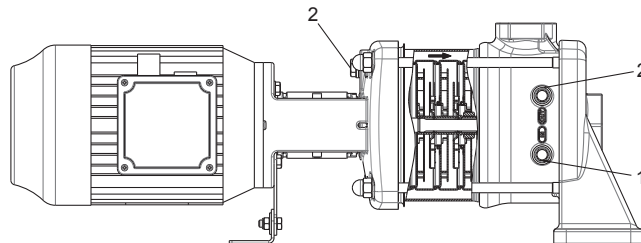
Anschlüsse zum Entleeren der Pumpe
